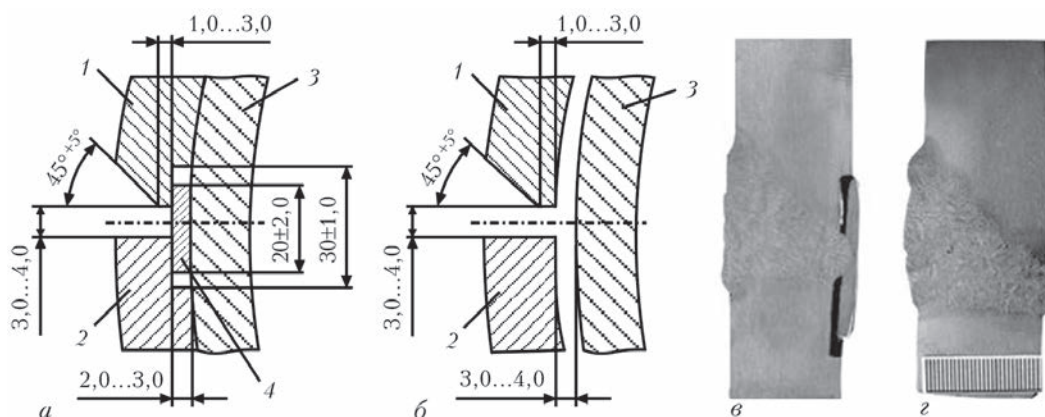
Продольные стыковые соединения усиливающих конструктивных элементов: а — разделка кромок для сварки с подкладной пластиной; б — разделка кромок для сварки «на весу»; в — макрошлиф соединения с подкладной пластиной (проволока DW-A55); з — макрошлиф соединения, выполненного проволокой Св-08Г2С «на весу» (1, 2 — стенка соответственно верхнего и нижнего усиливающего элемента; 3 — стенка газопровода; 4 — подкладная пластина)
